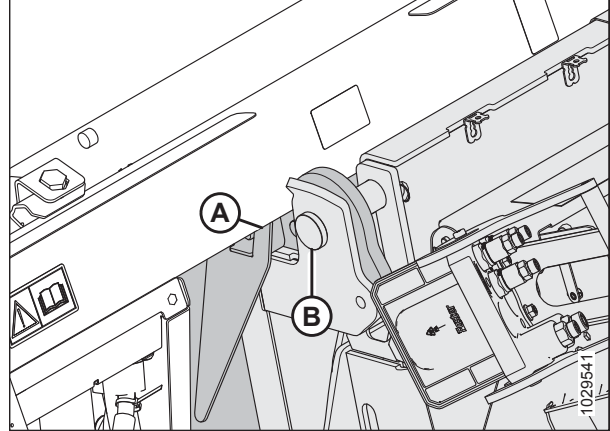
La poutre supérieure reposant sur le convoyeur
